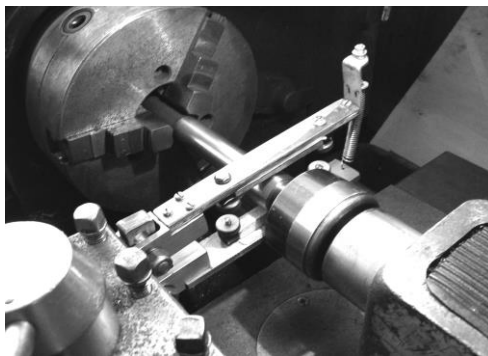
Установка устройства для чистовой обработки профильных деталей на токарном станке
